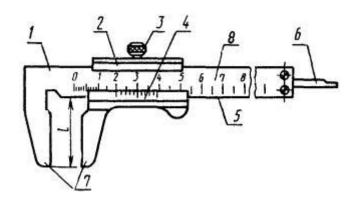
штангенциркуль односторонний с измерительными поверхностями из твердых сплавов с глубиномером
